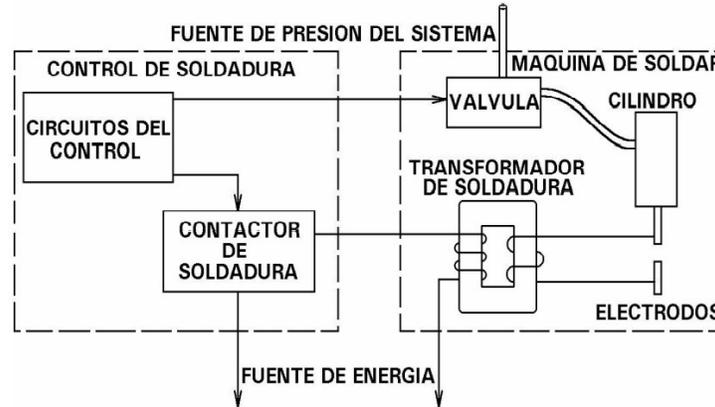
Elementos básicos de una máquina de soldadura por resistencia.
